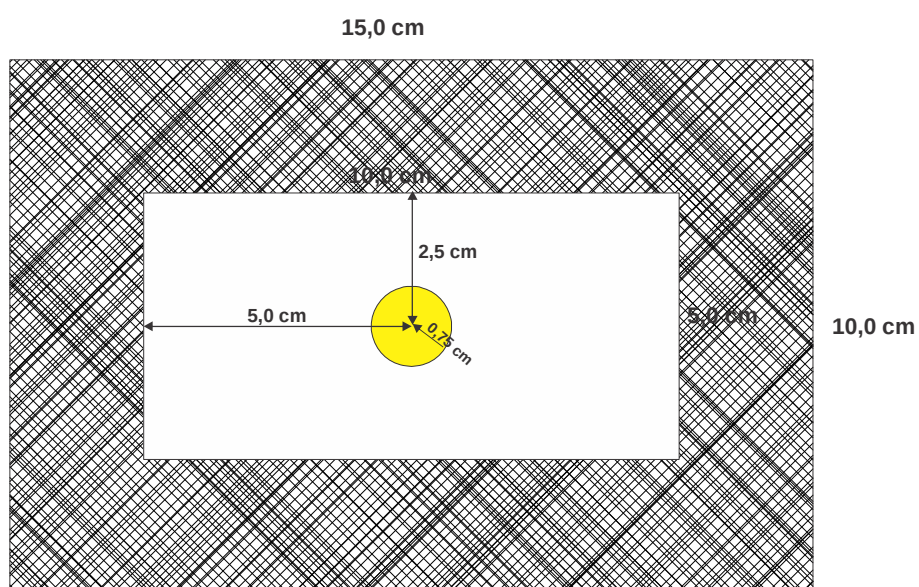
Diâmetro do furo de 1,5cm – posição central
